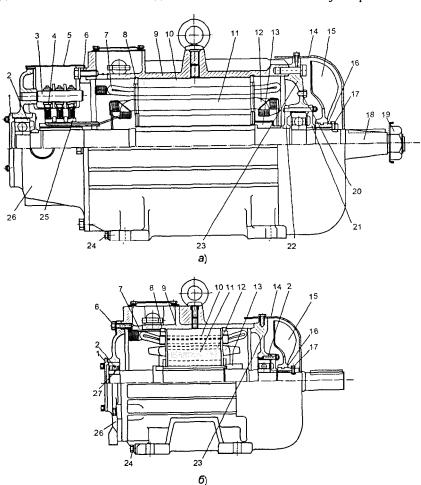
Крановые асинхронные электродвигатели: a — MT 41 с фазным ротором, b — MTK-11 с короткозамкнутым ротором; 1, 21 и 22 — крышки подшипниковых камер; 2 — подшипник; 3 — палец щеткодержателя; 4 — щеткодержатель; 5 — крышка окна в подшипниковом щите; 6 — болт крепления подшипникового щита; 7 — двухслойная обмотка статора; 8 — запорное кольцо сердечника; 9 — корпус статора; 10 — сердечник статора; 11 — сердечник ротора; 12 — обмотка ротора; 13 — втулка на валу, прижимающая сердечник ротора; 14 — кожух вентилятора; 15 — литой алюминиевый вентилятор; 16 — стальная втулка залитая в вентилятор; 17 — стопорный винт крепления вентилятора; 18 — конический рабочий конец вала со шпонкой; 19 — затяжная гайка; 20 — болт, закрывающий отверстие в подшипниковом щите для измерения воздушного зазора между статором и ротором; 23 и 26 — подшипниковые щиты; 24 — болт для присоединения заземления; 25 — контактные кольца; 27 — защитная шайба шарико-
